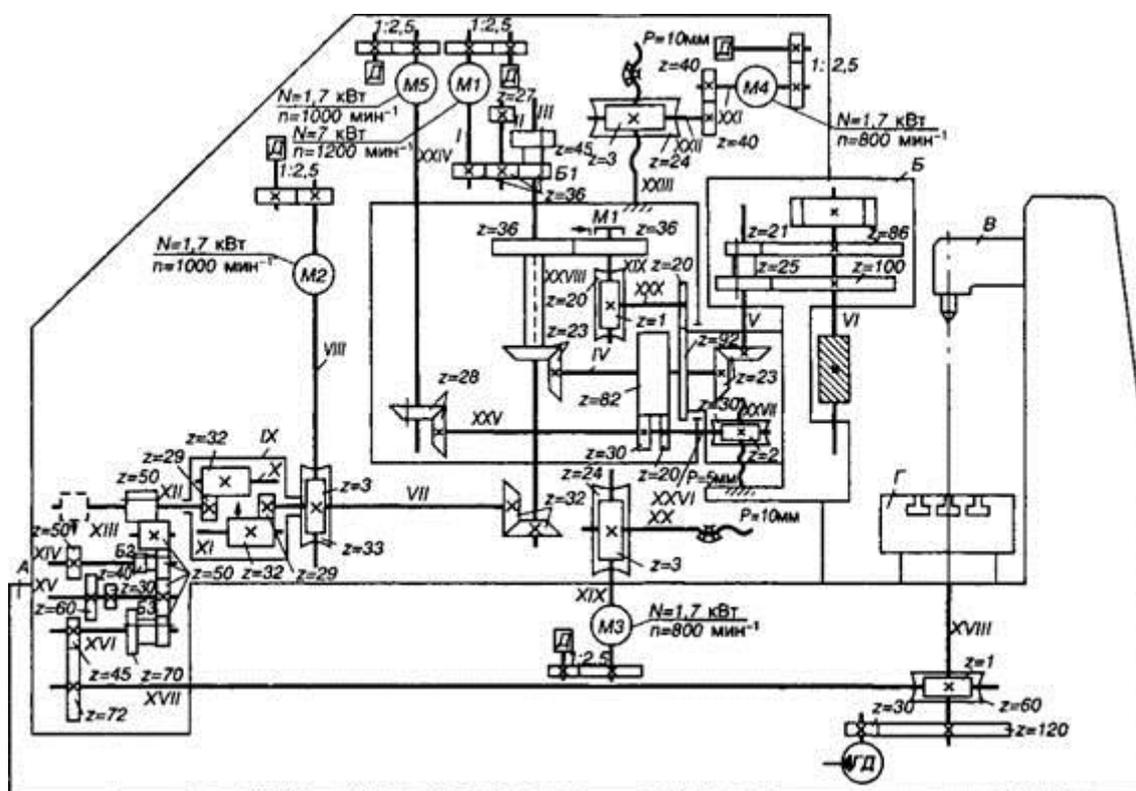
Кинематическая схема зубофрезерного полуавтомата 53A20Ф4 с ЧПУ
